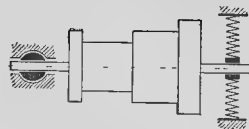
Схема устройства станка для динамической балансировки (вид сверху).
